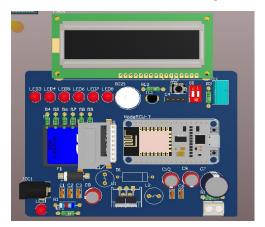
Sơ đồ mạch in PCB mạch Slave
